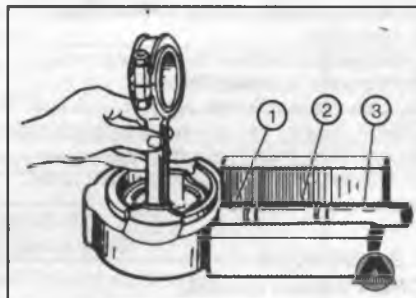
Приспособление для выпрессовки и запрессовки поршневого пальца: 1. Направляющая; 2. Палец; 3. Плунжер.
